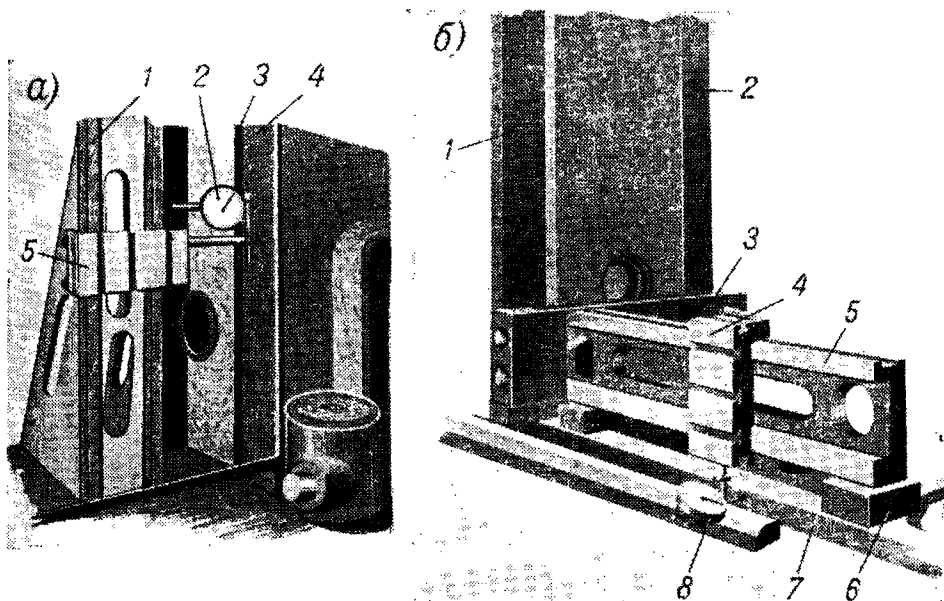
Проверка направляющих консоли фрезерного станка: а — на перпендикулярность зеркалу станины; б — на правильность положения относительно боковой направляющей станины
